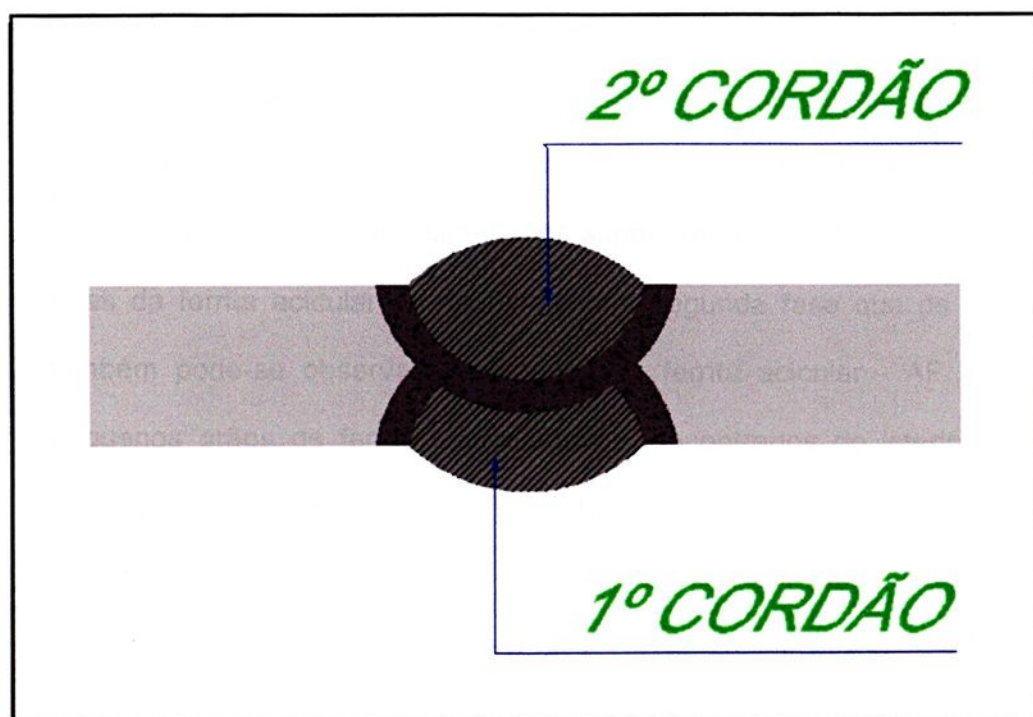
Representação esquemática da junta soldada mostrando as diferentes regiões produzidas na soldagem.
